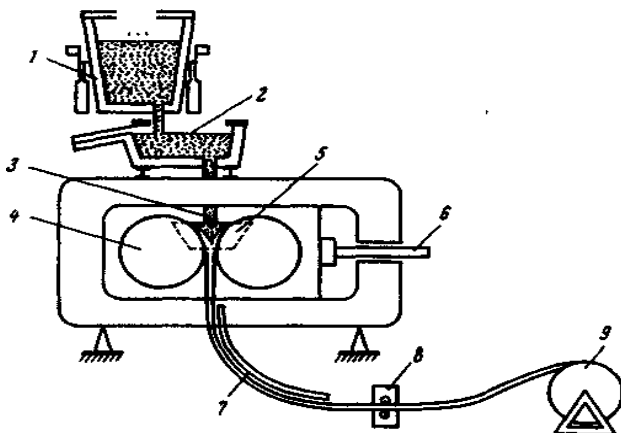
Схема двухвалковой УНРС прямого получения листа: 1 - ковш; 2 - разливочный узел; 3 - погружной стакан; 4 - валки; 5 - уплотнение; 6 - регулятор нагрузки; 7 - направляющий желоб; 8 - приемные валки; 9 - сматыватель
